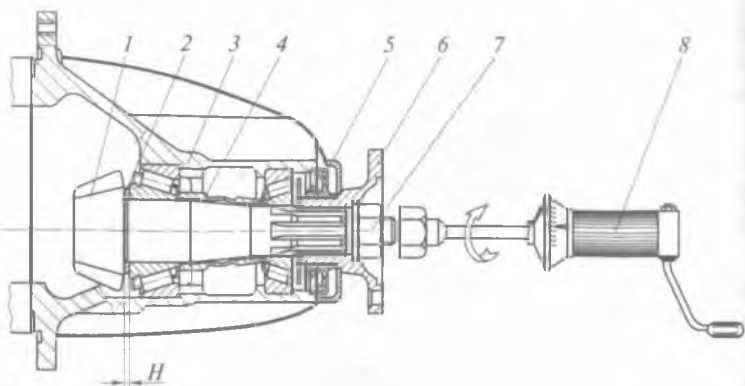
Схема проверки момента проворачивания ведущего колеса (без дифференциала):
